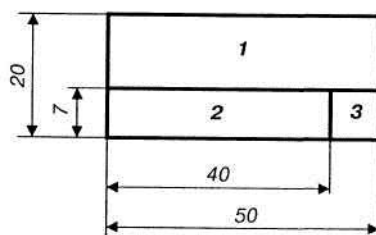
Условное обозначение детали и сборочной единицы:
